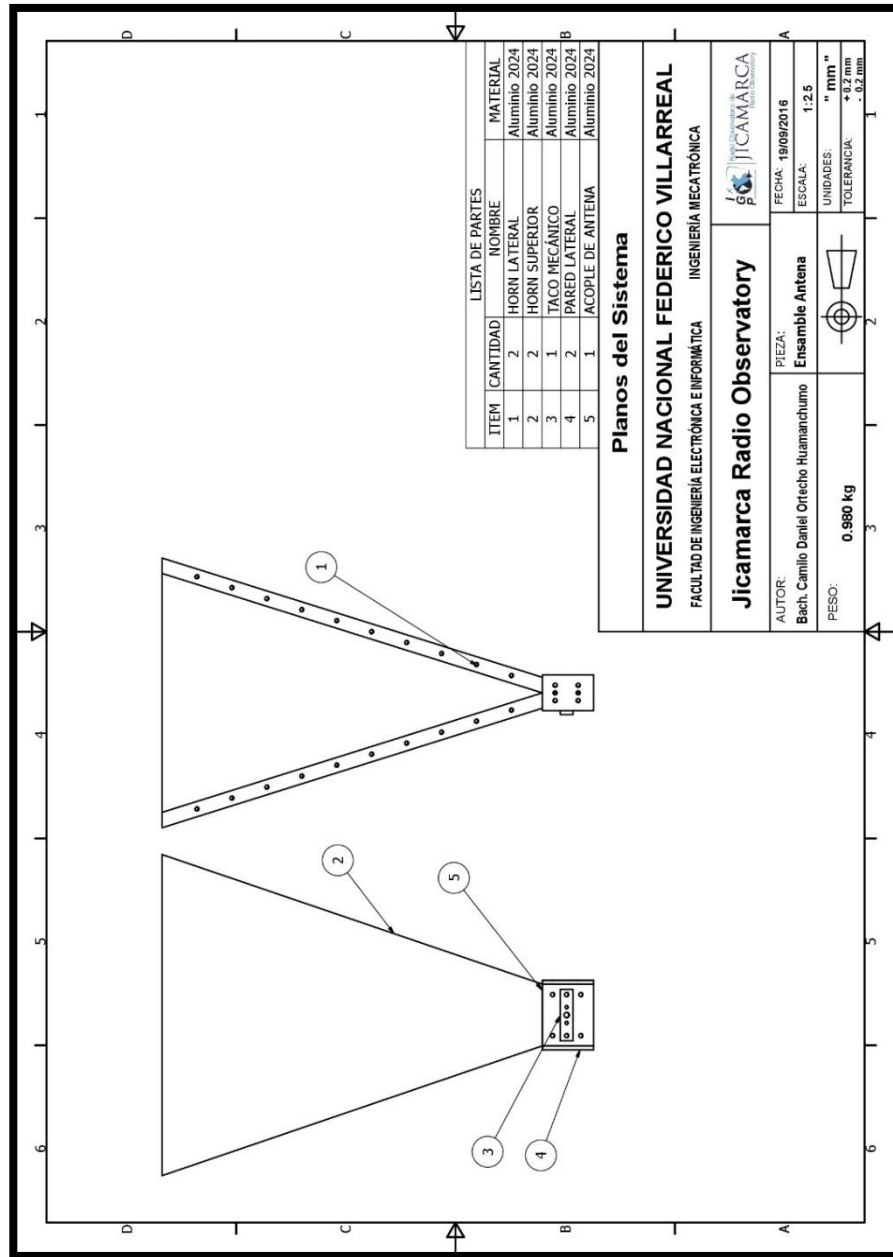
Plano del ensamble de la antena (Fuente: el autor)
